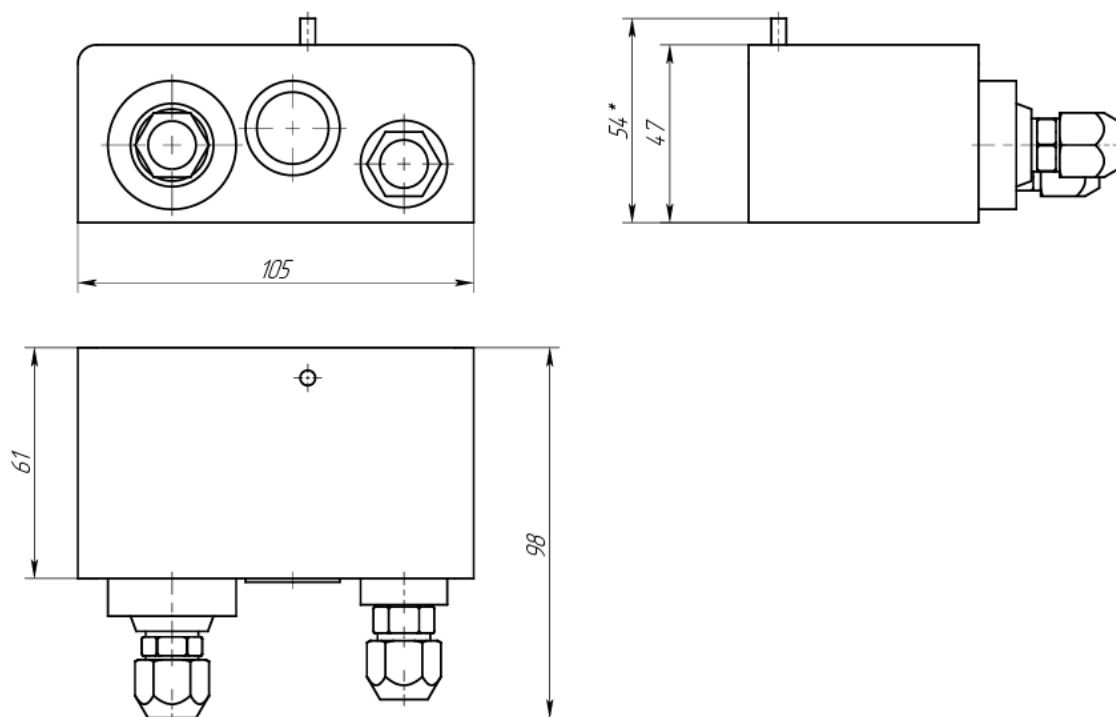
Габаритные и присоединительные размеры реле давления типа РДф-2
